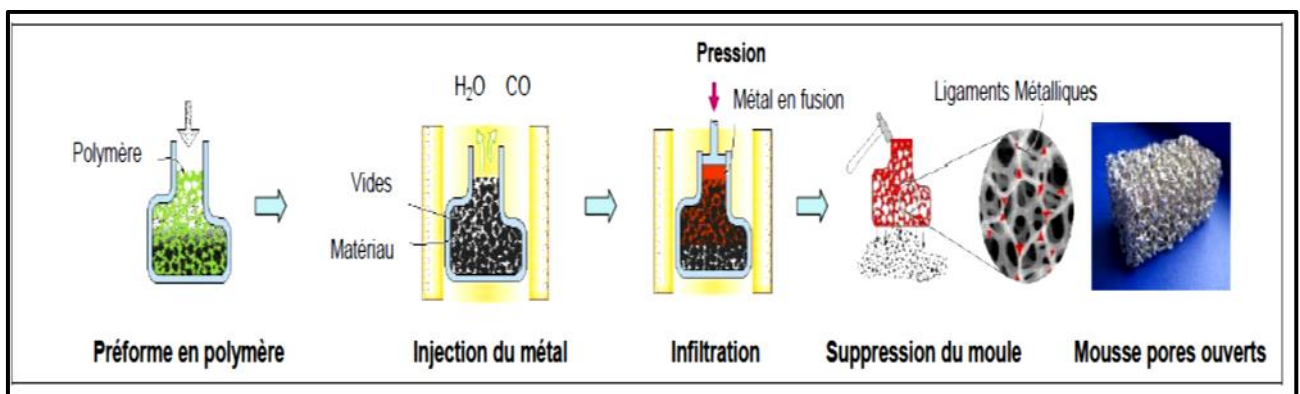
Procédé de fabrication des mousses d'aluminium par écoulement d'infiltration [11].
